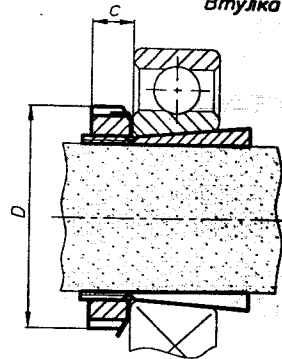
Закрепление внутреннего кольца подшипника на валу с использованием закрепительной втулки
